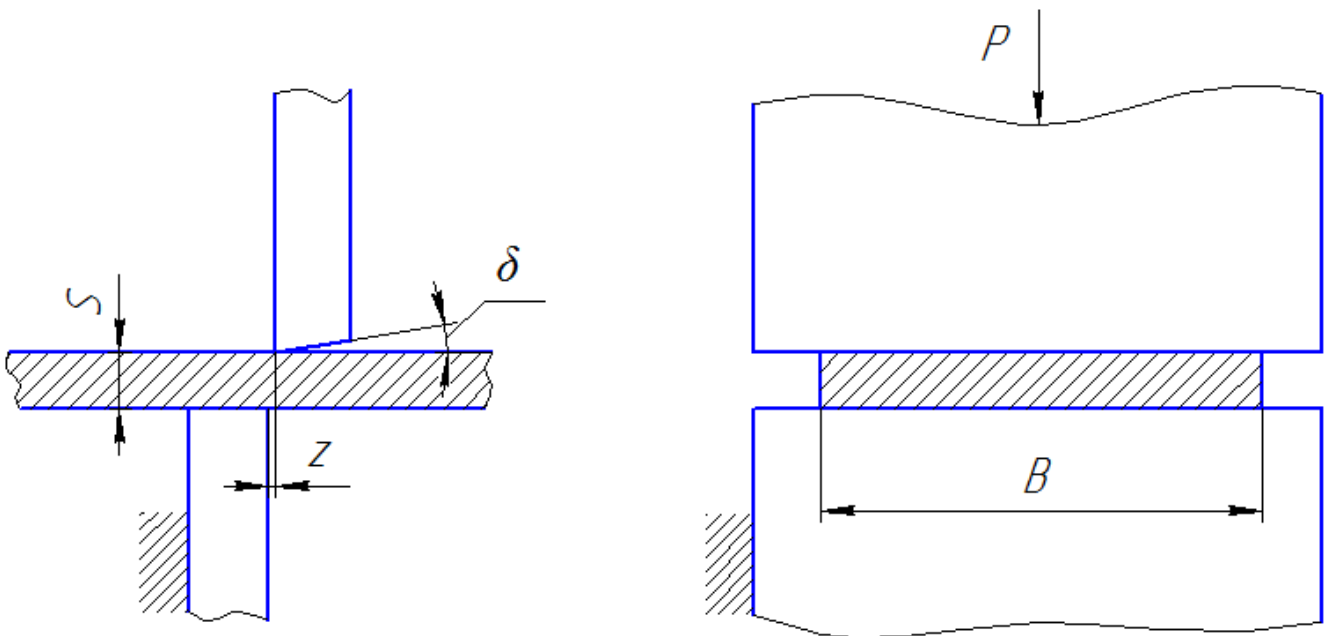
Схема різки ножицями з паралельними ножами
